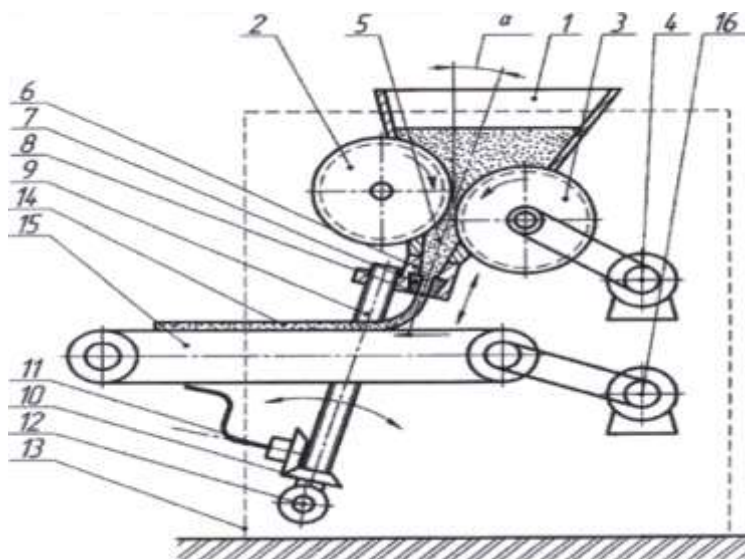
Устройство для формования заготовок пищевых продуктов методом экструзии
